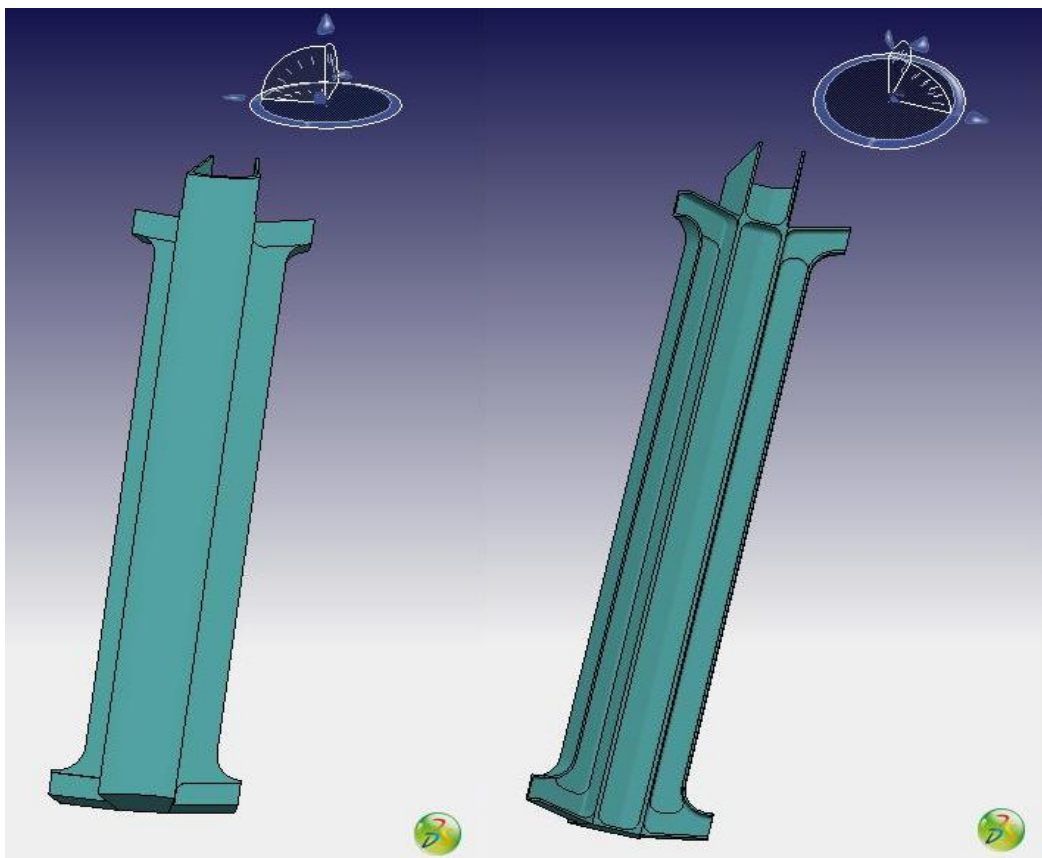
Proposta de alteração da viga central da estrutura.
